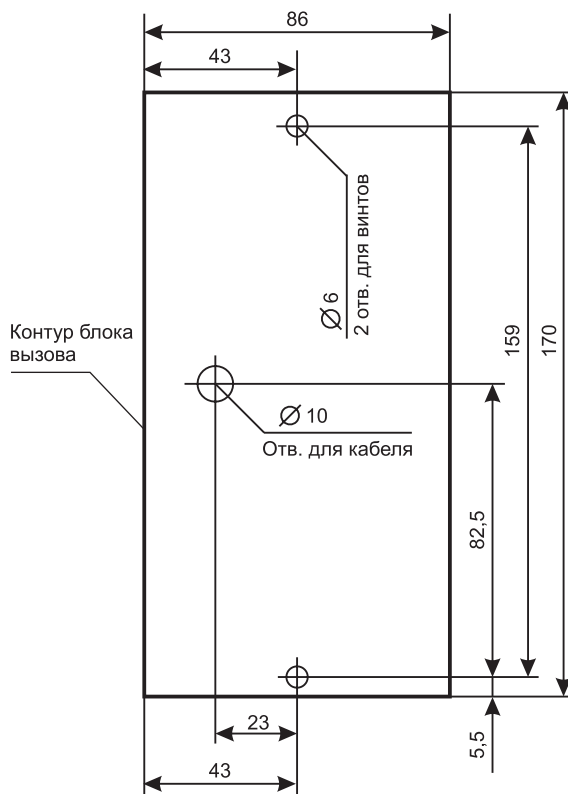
Расположение и размеры отверстий для установки блока вызова
